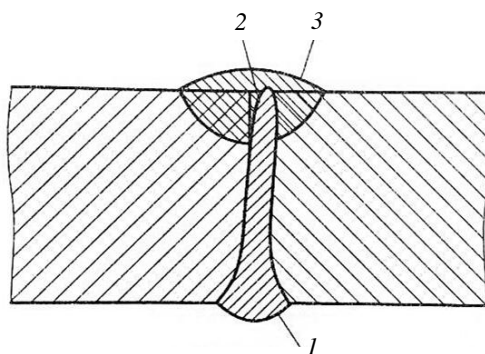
Заварка поверхностного дефекта: 1 – основной проход; 2 – непровар; 3 – подварочный проход
